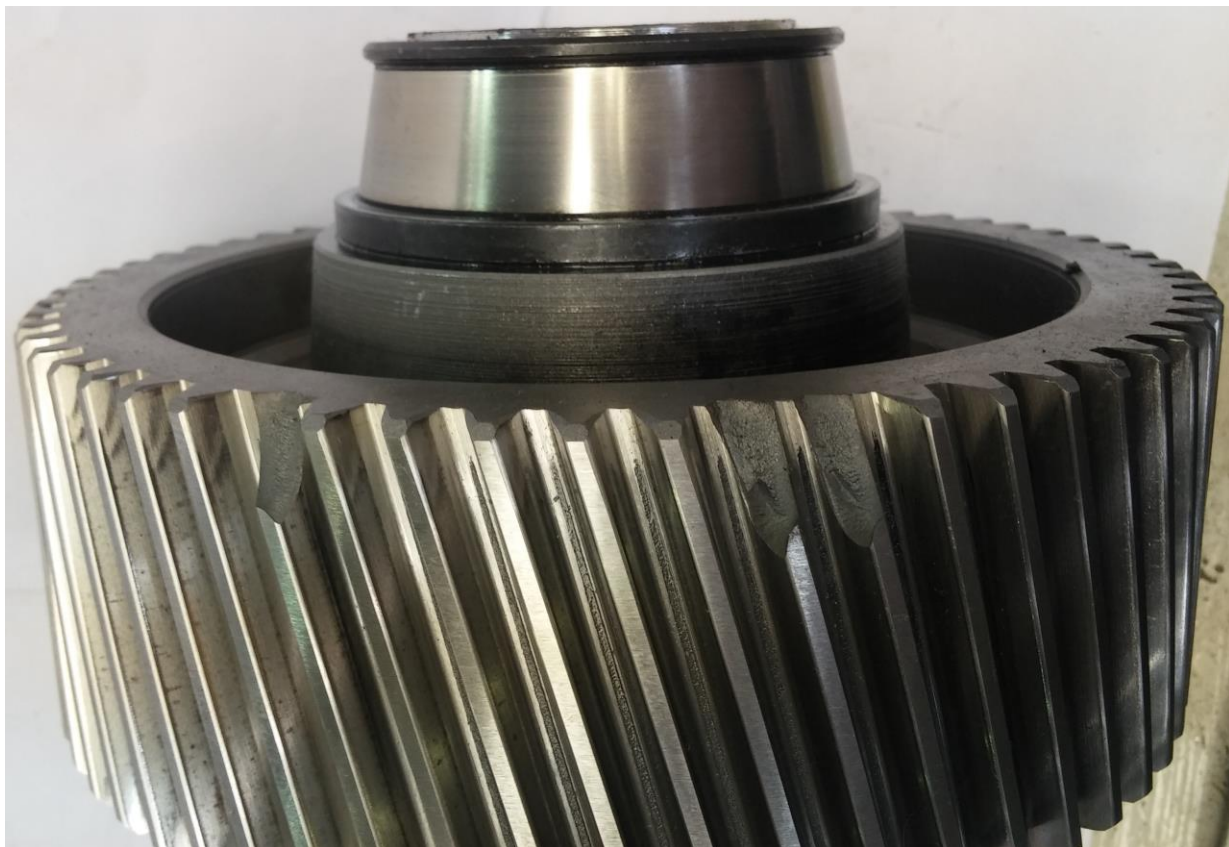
Внешний вид выходного колеса редуктора с эвольвентным зубчатым зацеплением после испытаний
